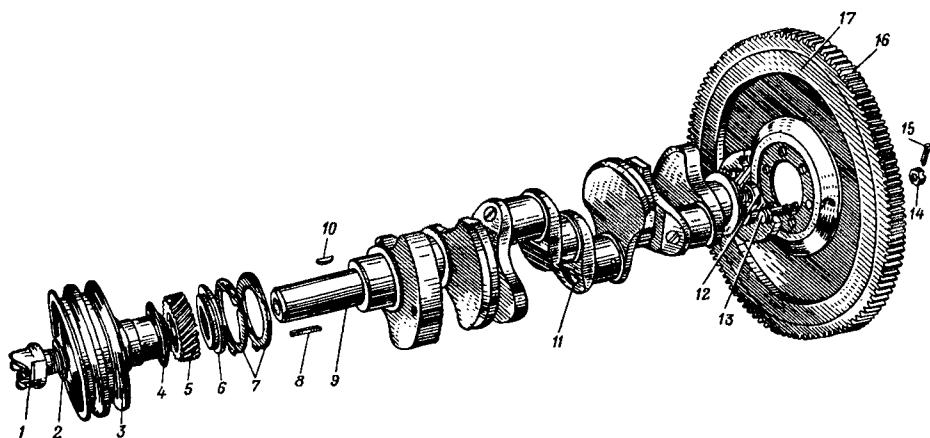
Коленчатый вал двигателя ЗИЛ-131:
